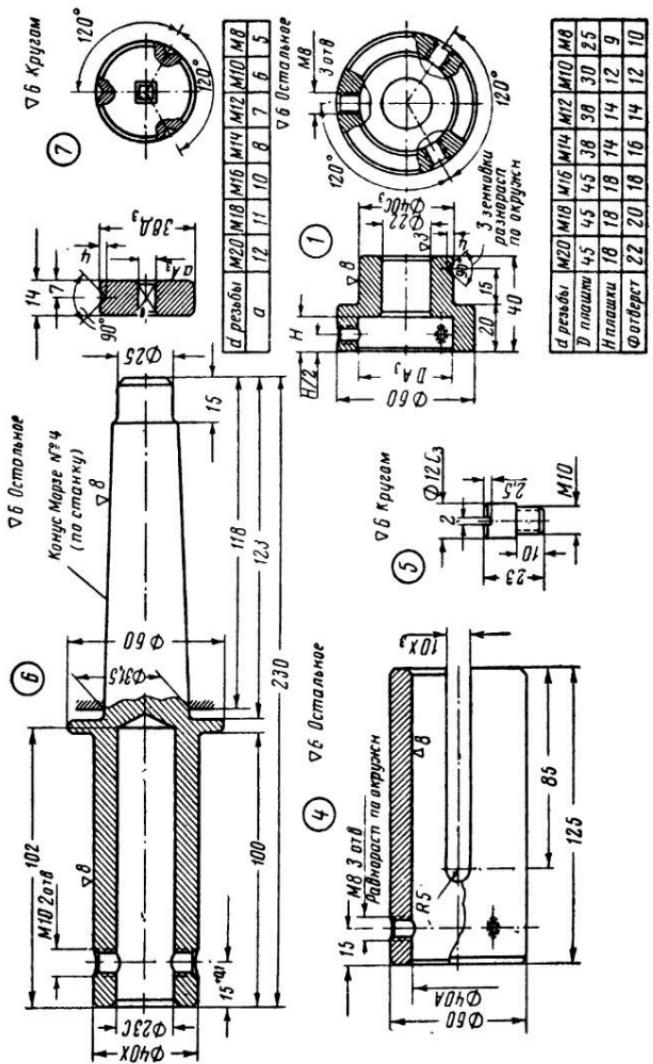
Детали универсального приспособления для нарезания резьбы: 1 — сменный держатель; 4 — скользящая втулка; 5 — складной втулки; 6 — опорный штырь; 7 — корпук; 7 — сменный вкладыш.
